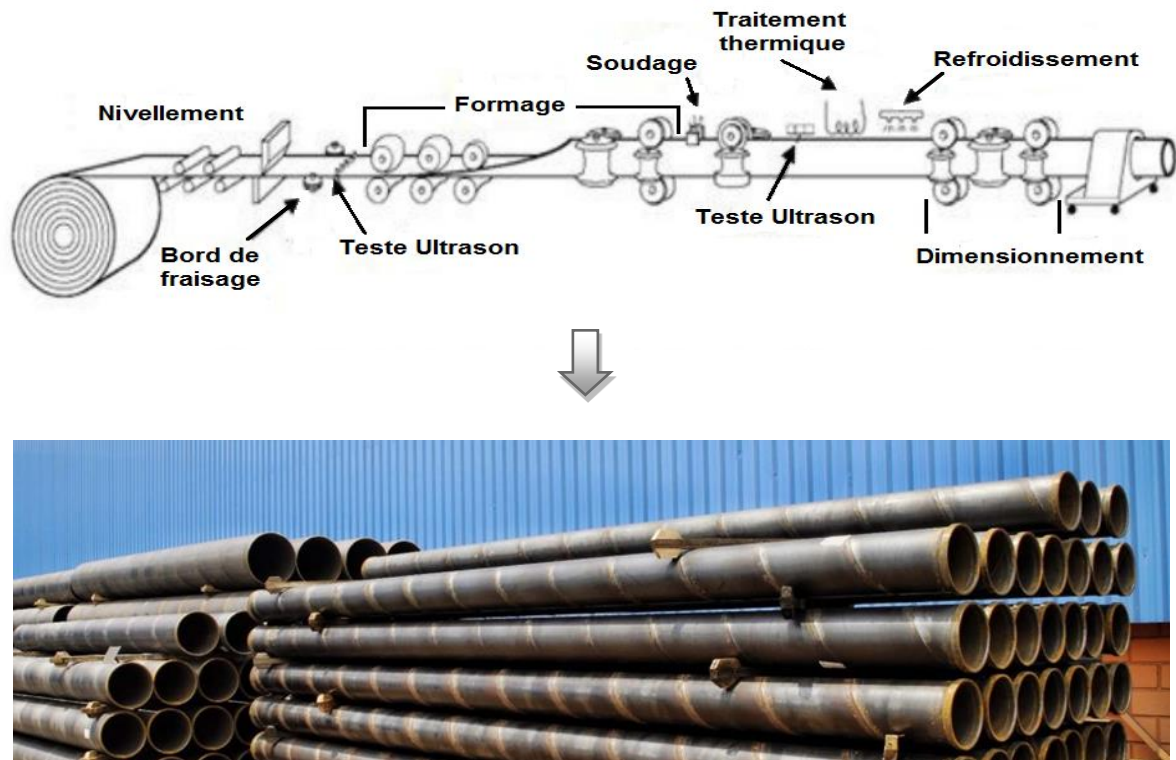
Technique de fabrication des tubes soudés en spirale [ZAZ 17]
